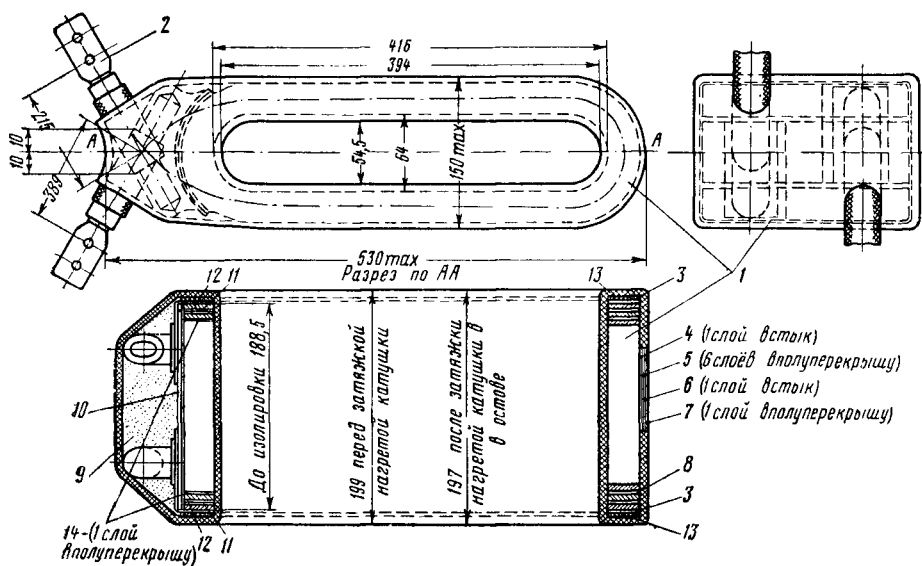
Кагушка обмотки якоря тягового двигателя типа ДПЭ-400А и Б
